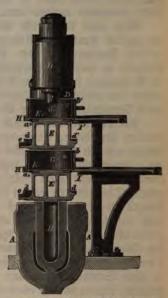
Hybraulische Topfs presse (Seitenansicht und Querschnitt).
